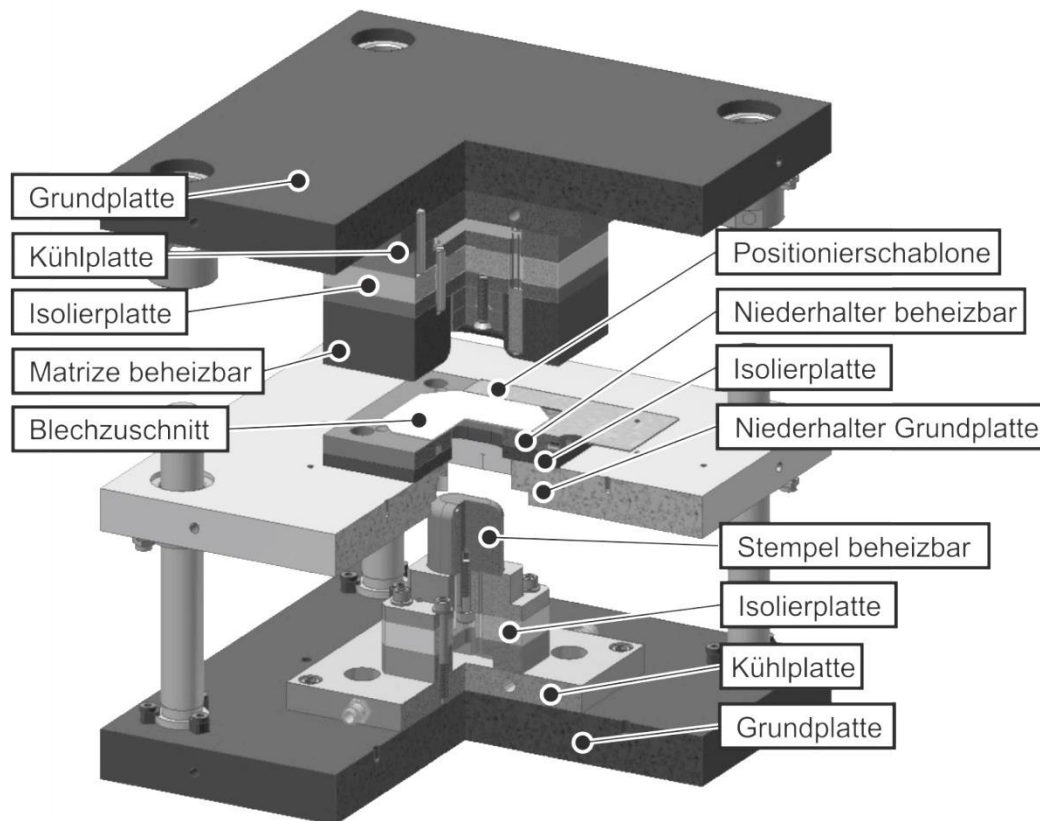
Tiefziehwerkzeug für die Blechumformung bei erhöhten Temperaturen
